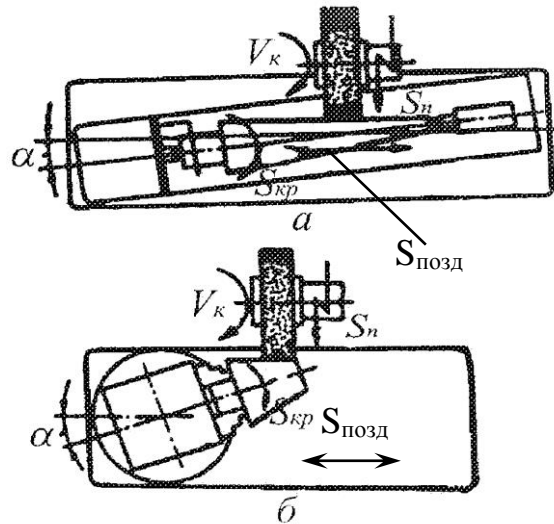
Схеми обробки конічних поверхонь на круглошліфувальних верстатах
